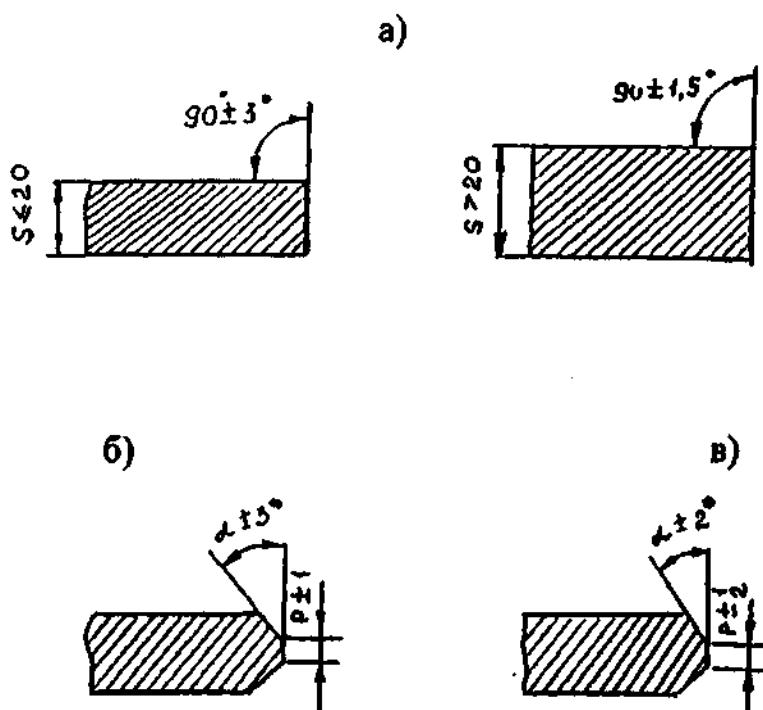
Допускаемые отклонения при подготовке кромок под сварку:
